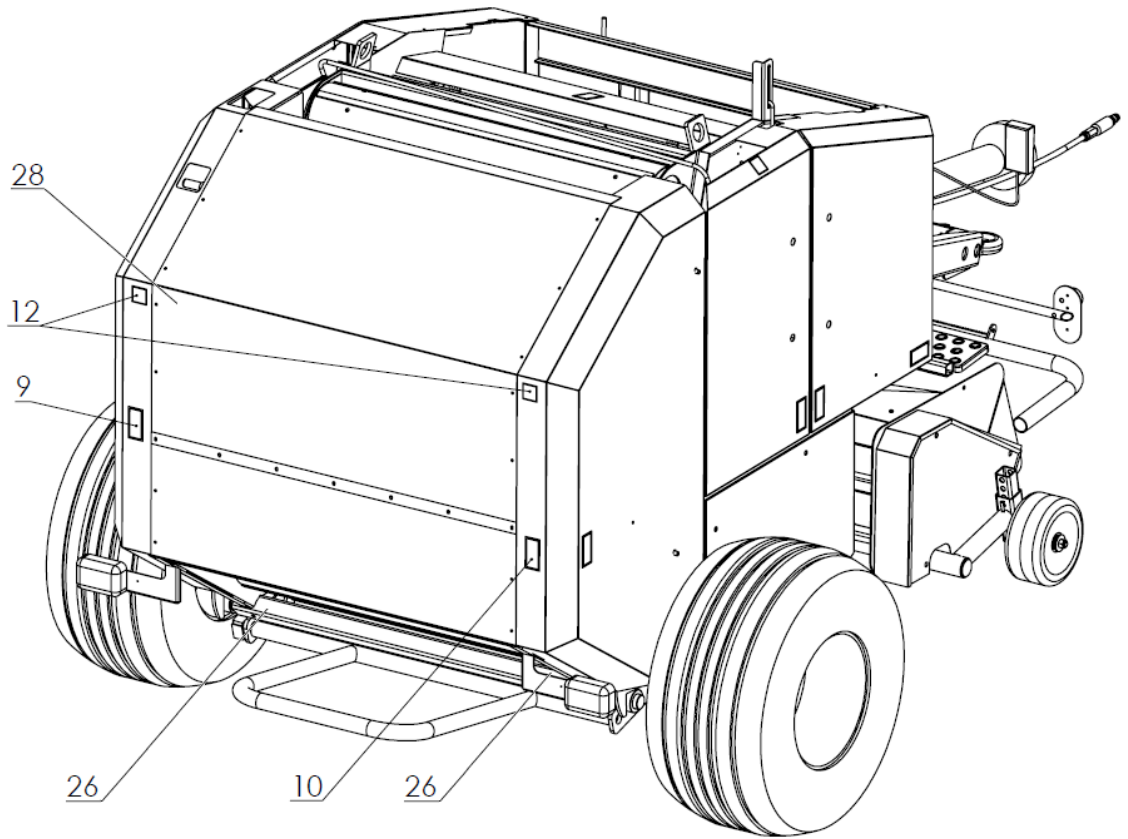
Disposition des symboles de sécurité sur la machine – arrière
